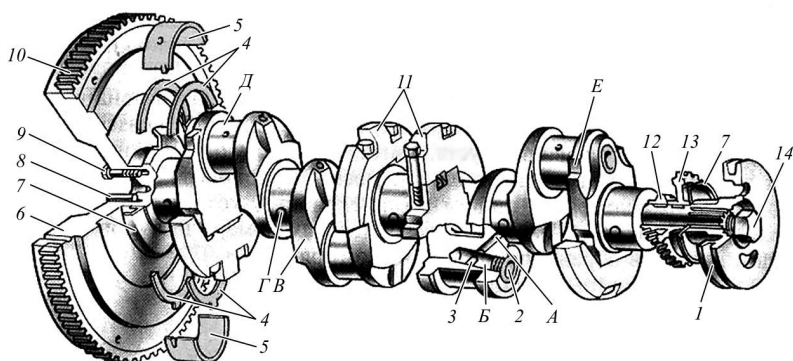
Коленчатый вал двигателя Д-245 с сопряженными деталями: *А* – канал подвода масла; *Б* – полость центробежной очистки масла; *В* – щеки кривошипа; *Г* – коренные шейки коленчатого вала; *Д* – шатунные шейки коленчатого вала; *Е* – галтель; 1 – шкив; 2 – пробка; 3 – трубка; 4 – упорные полукольца; 5 – вкладыш коренного подшипника; 6 – маховик; 7 – маслоотражатель; 8 – установочный штифт; 9 – болт крепления маховика; 10 – зубчатый венец; 11 – противовесы; 12 – шестерня коленчатого вала; 13 – ведущая шестерня привода масляного насоса; 14 – болт для проворачивания вала
